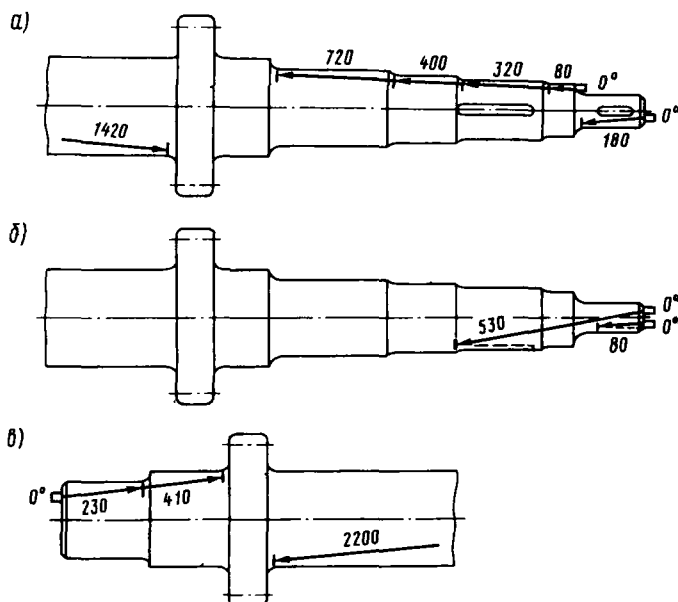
Схемы и зоны контроля прямым искателем со стороны торцов главного приводного вала эскалатора Н-10-20
